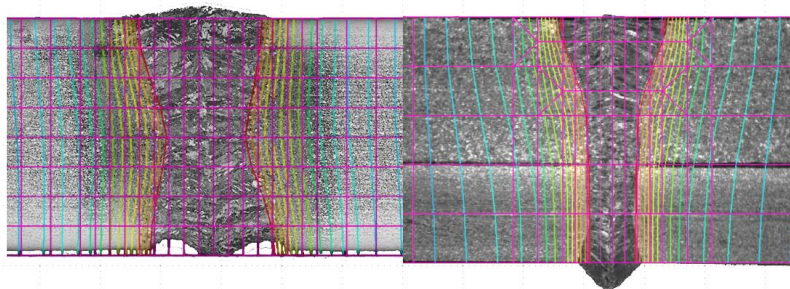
Wärmequellenabgleich am Beispiel von zwei Laserschweißnähten
